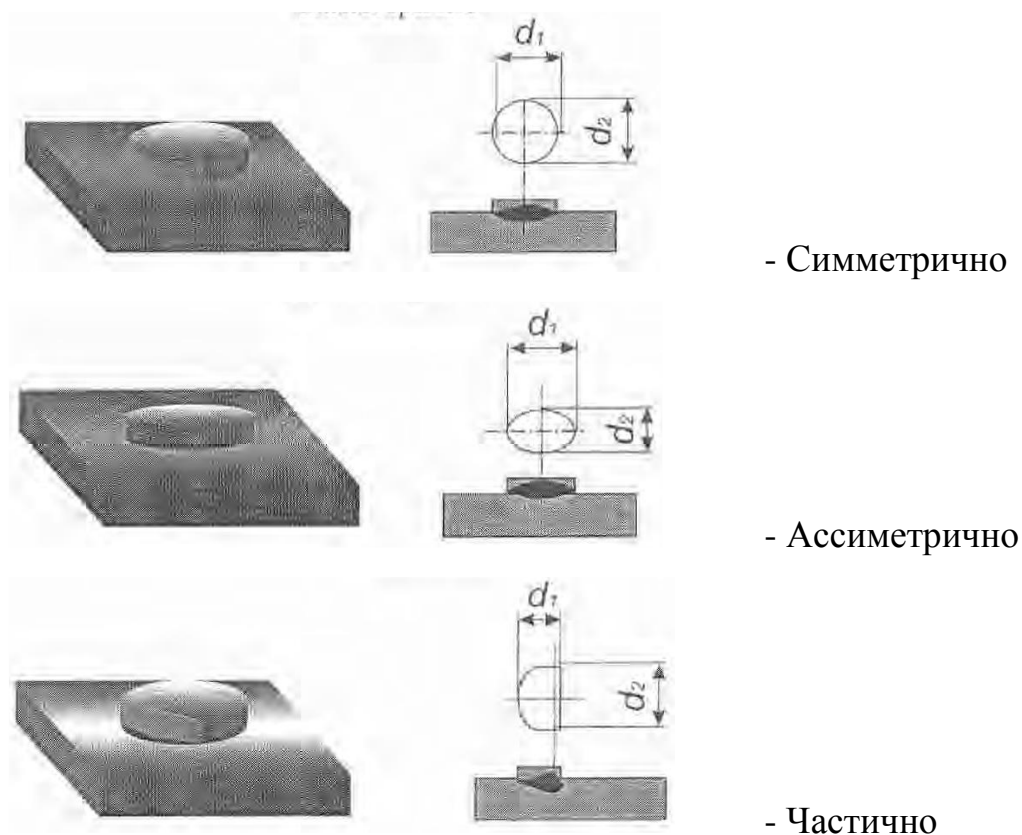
Сварная точка с разрушением и вырывом
